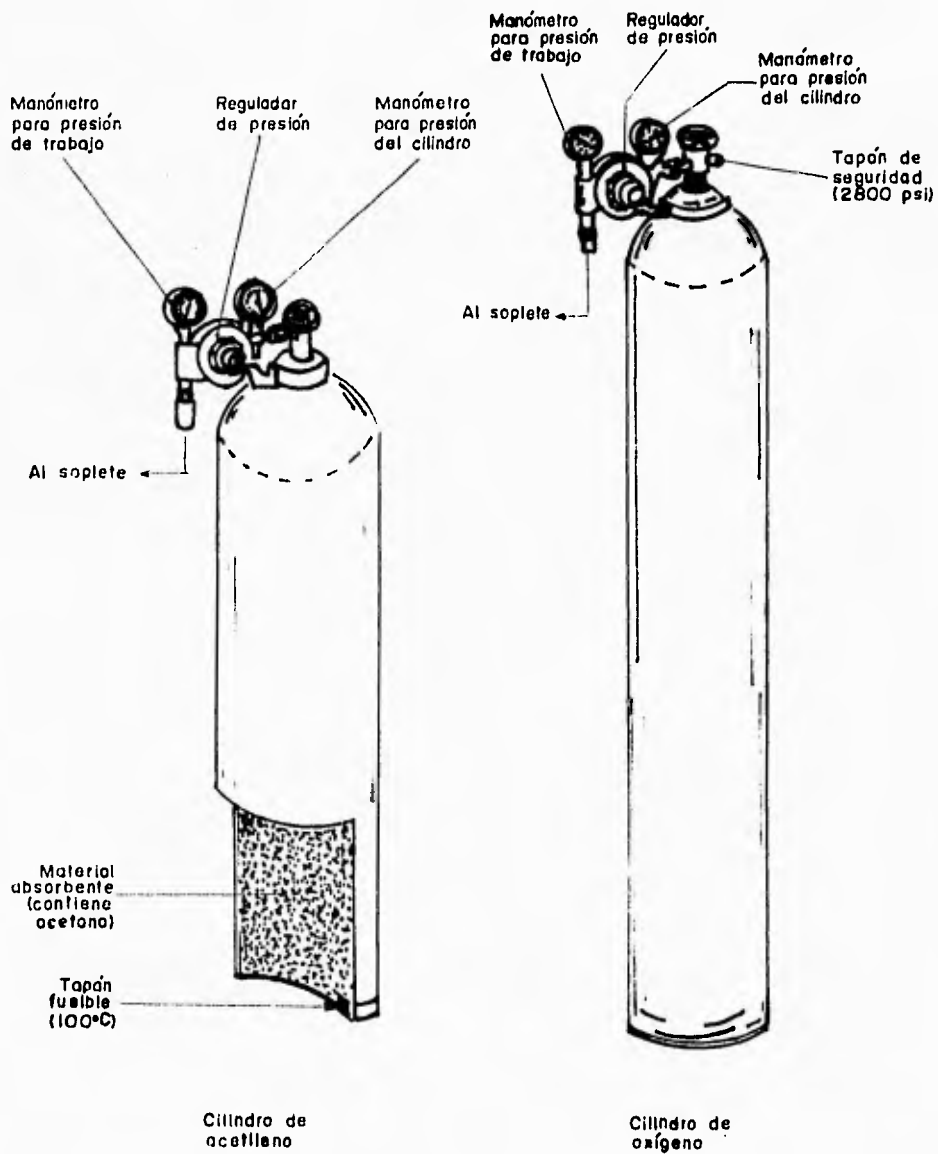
Cilindros de gas para soldadura oxiacetilénica
